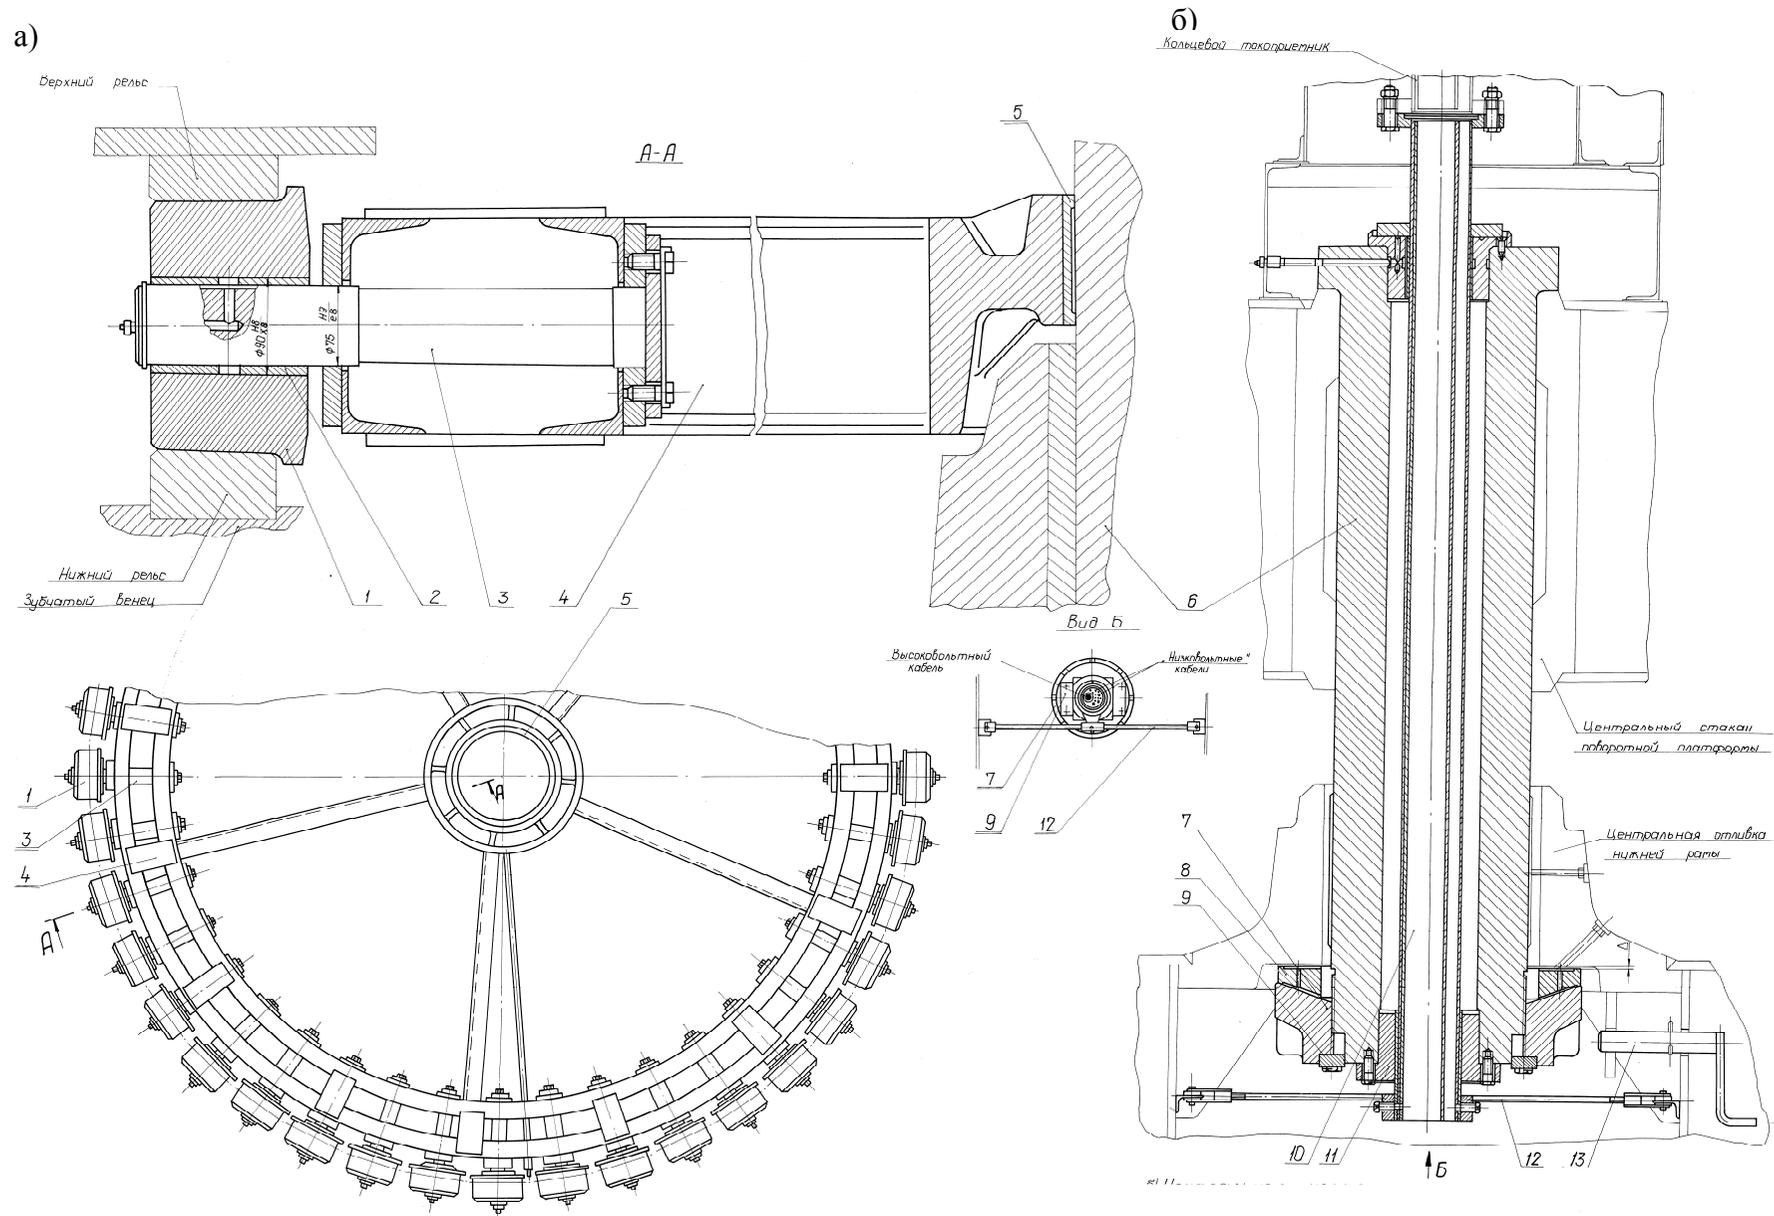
Опорно-поворотное устройство: а – роликовый круг; б – центральная цапфа
